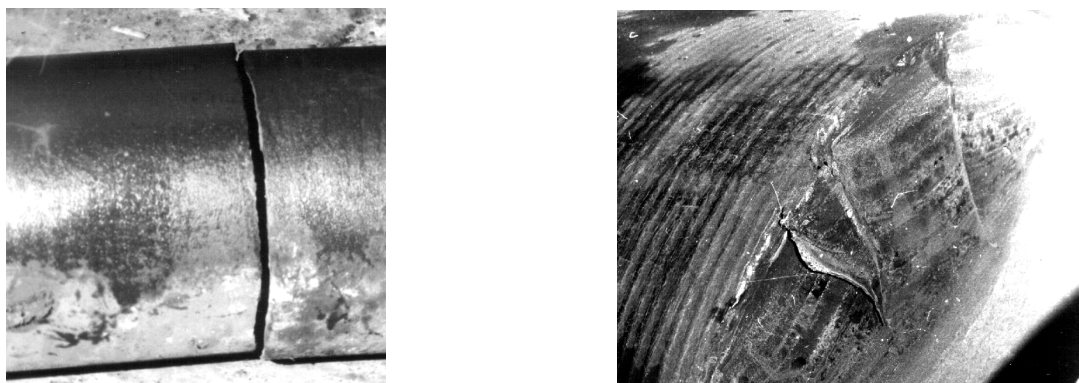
Внешний вид разрушенного прокатного инструмента, упрочненного наплавкой
